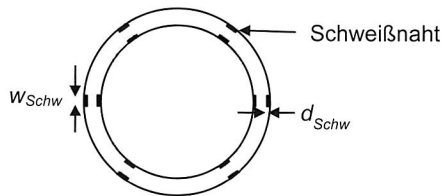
Ringkernmuster mit paarweise angeordneten Schweißnähten
